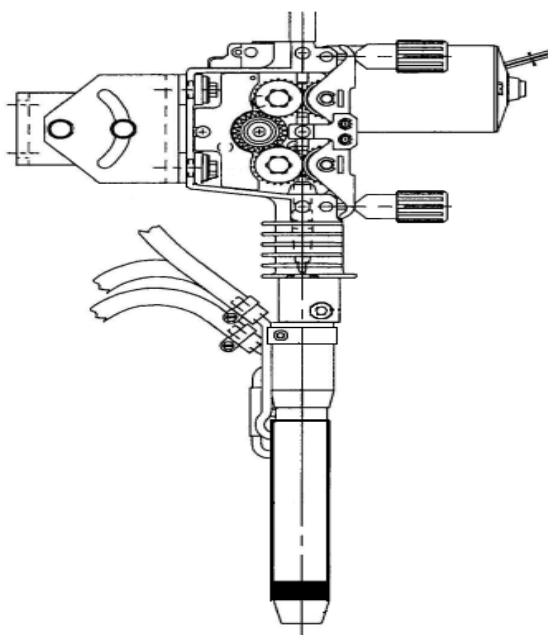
Головка для сварки в защитных газах
